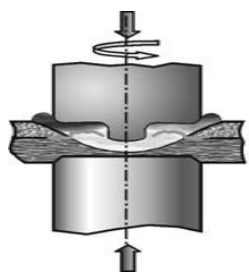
Схема точечной сварки трением, используемая фирмой MAZDA, и устройство для ее выполнения
